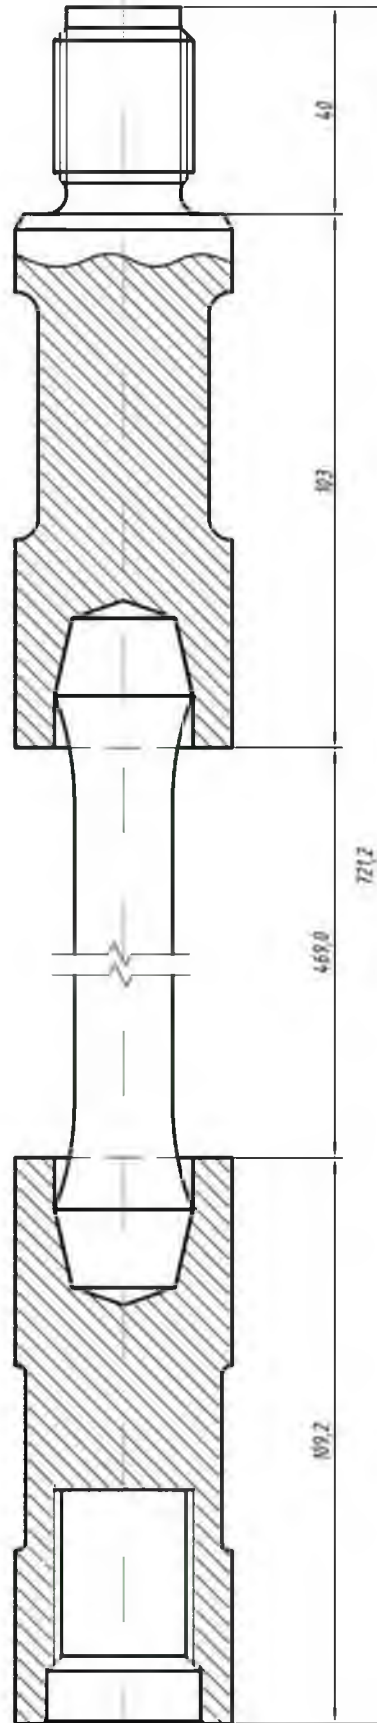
г - Штанга с цилиндрическим профилем резьбы в сборе.
